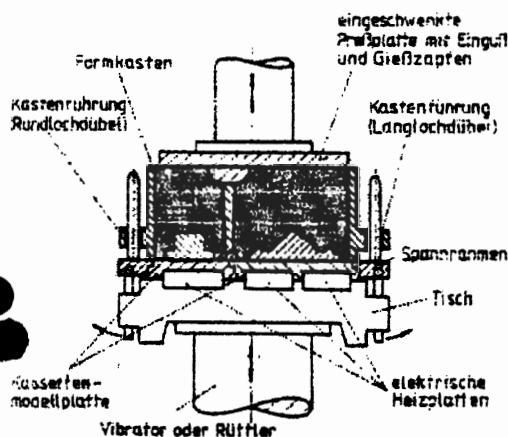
Rüttel-Preß-Formmaschine in Position Ende Verdichten des Formstoffes im Oberkasten.
